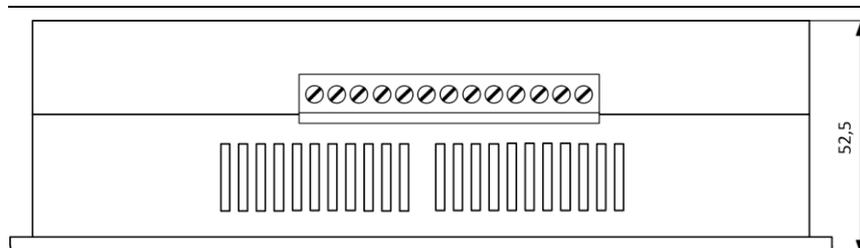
Габаритный чертеж ПЛК, вид снизу
